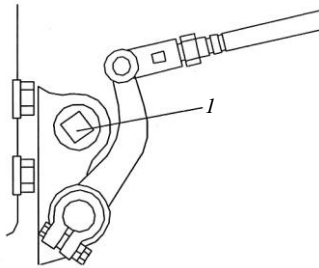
Схема смазки подшипника отводки сцепления: 1 – пробка
